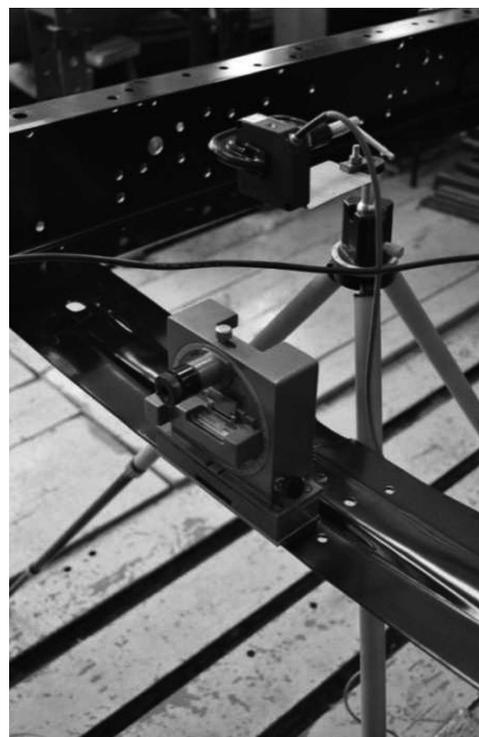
Установка квадранта на поперечине и лазерного датчика перемещений на стойке
